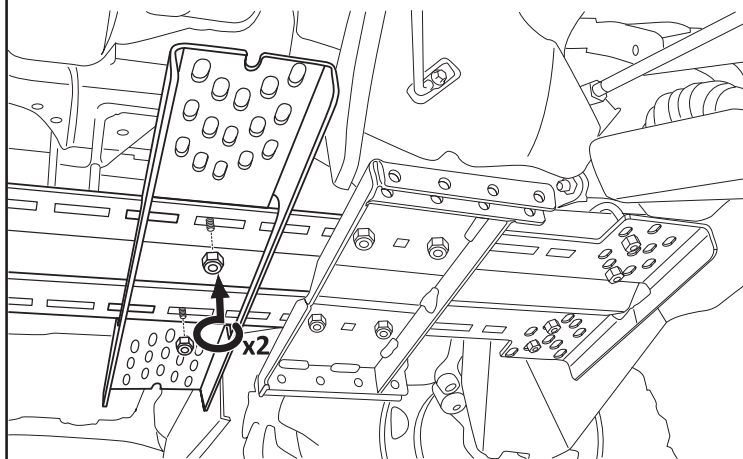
Fissare senza stringere la piastra di contatto posteriore al fissaggio con i bulloni a testa tonda.
